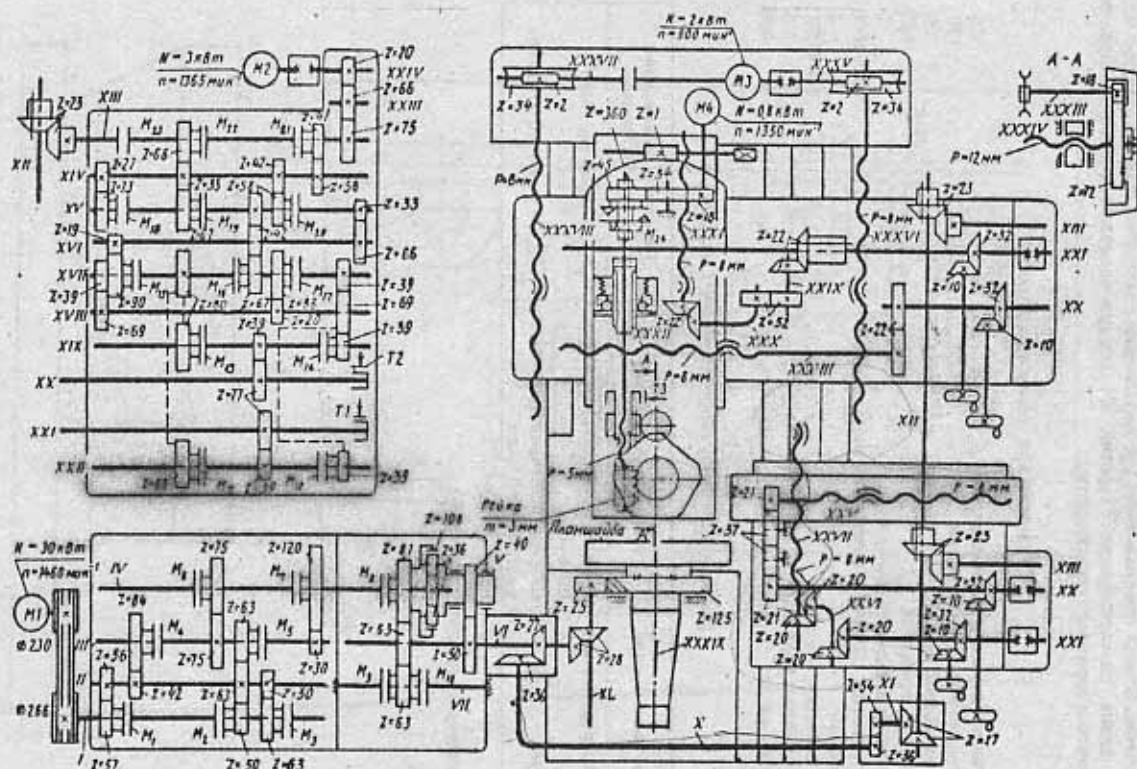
Кинематическая схема токарно-карусельного станка мод. 1512
